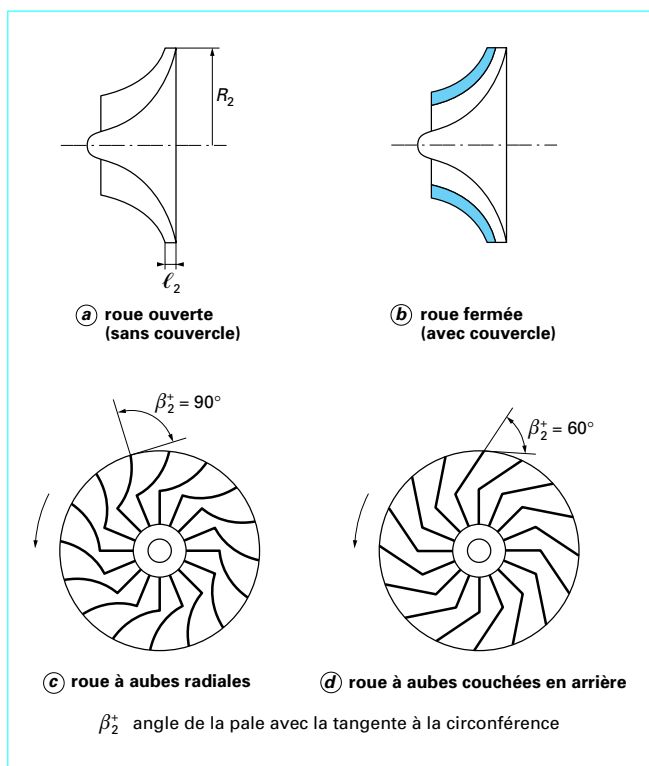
Roues mobiles centrifuges ouvertes ou fermées, à aubes radiales ou couchées en arrière
